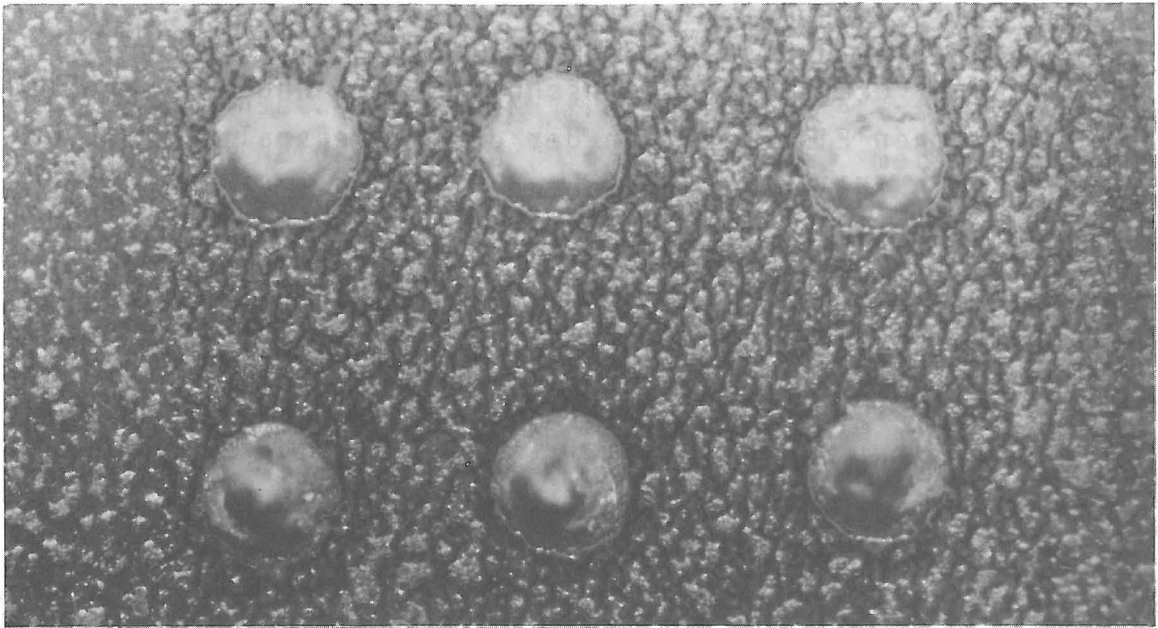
Einblick in den Walzenspalt bei stehenden Walzen
